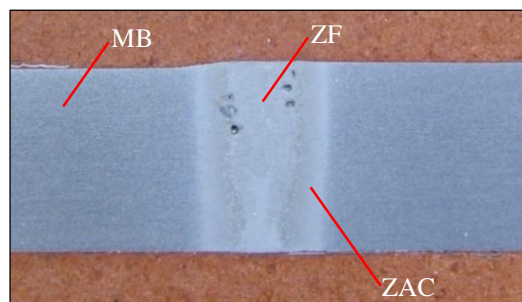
Macrografia do CP identificado por GM do processo de soldagem GMAW.
